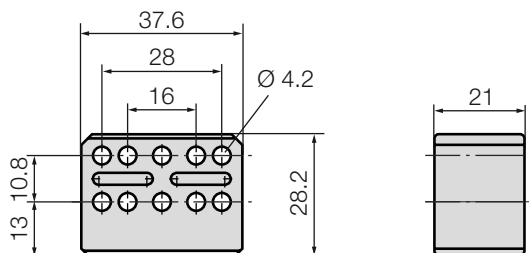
Einbaumaße Positionsgeber BTL6-A-3800-2
